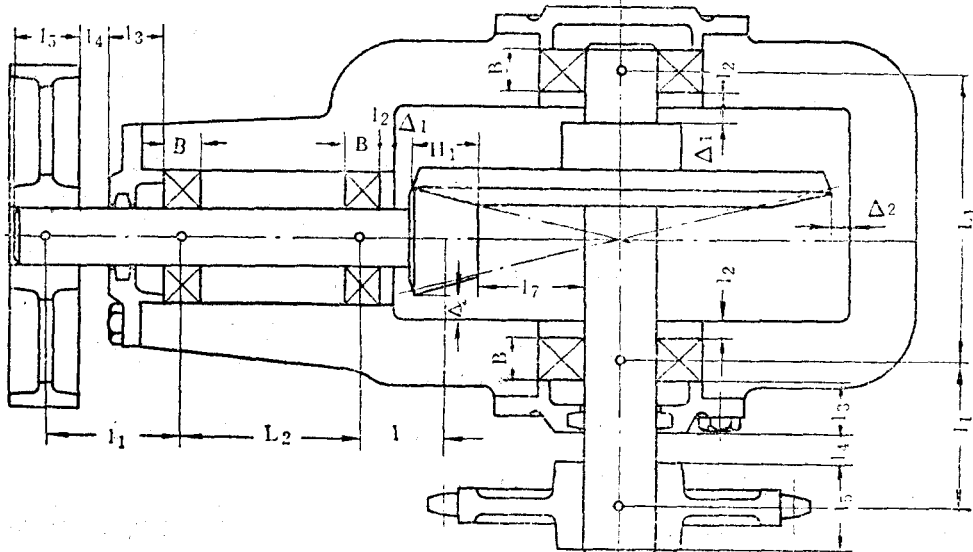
单级圆锥齿轮减速器零件的位置尺寸
